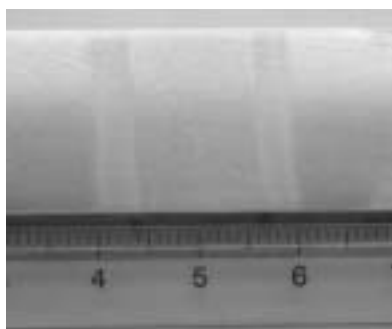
Макрошлиф сварного соединения (плоскость)
